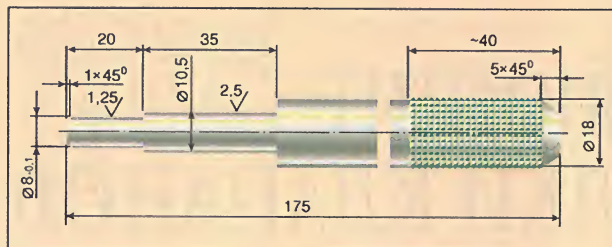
Оправка для запрессовки и выпрессовки направляющих втулок клапанов "Ауди-100".
